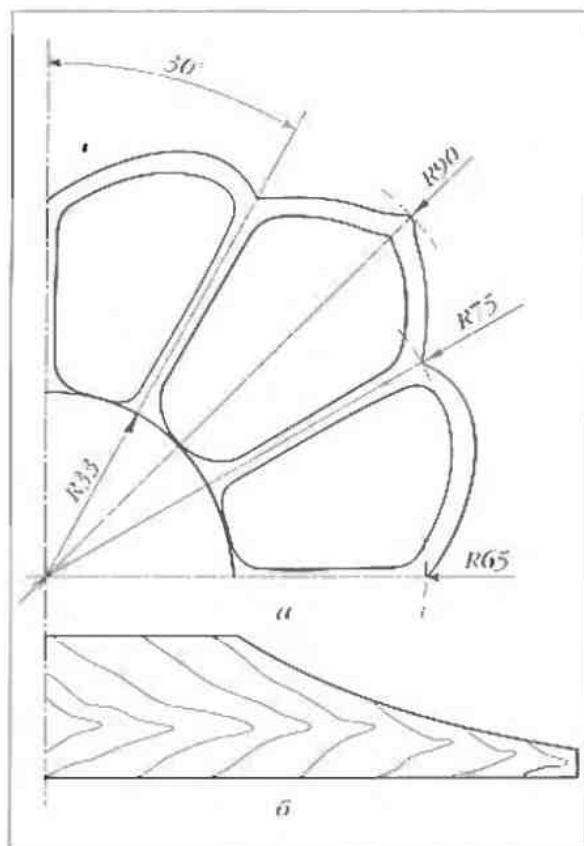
Шаблон основания вазы (масштаб 0,85:1): а – вид в плане; б – сечение заготовки
